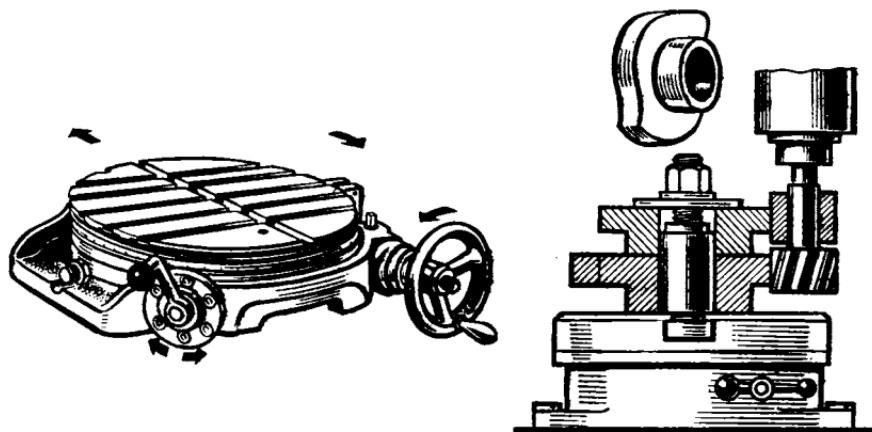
Круглый поворотный стол и его применение при фрезеровании по накладному копиру.
